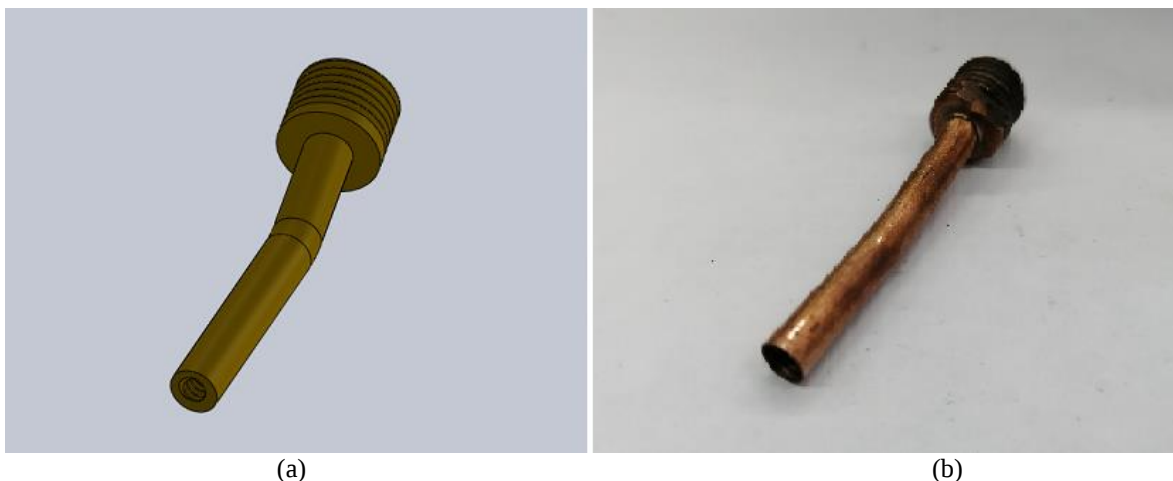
(a) Tubo direcionador projetado. (b) Tubo direcionador fabricado de cobre.
